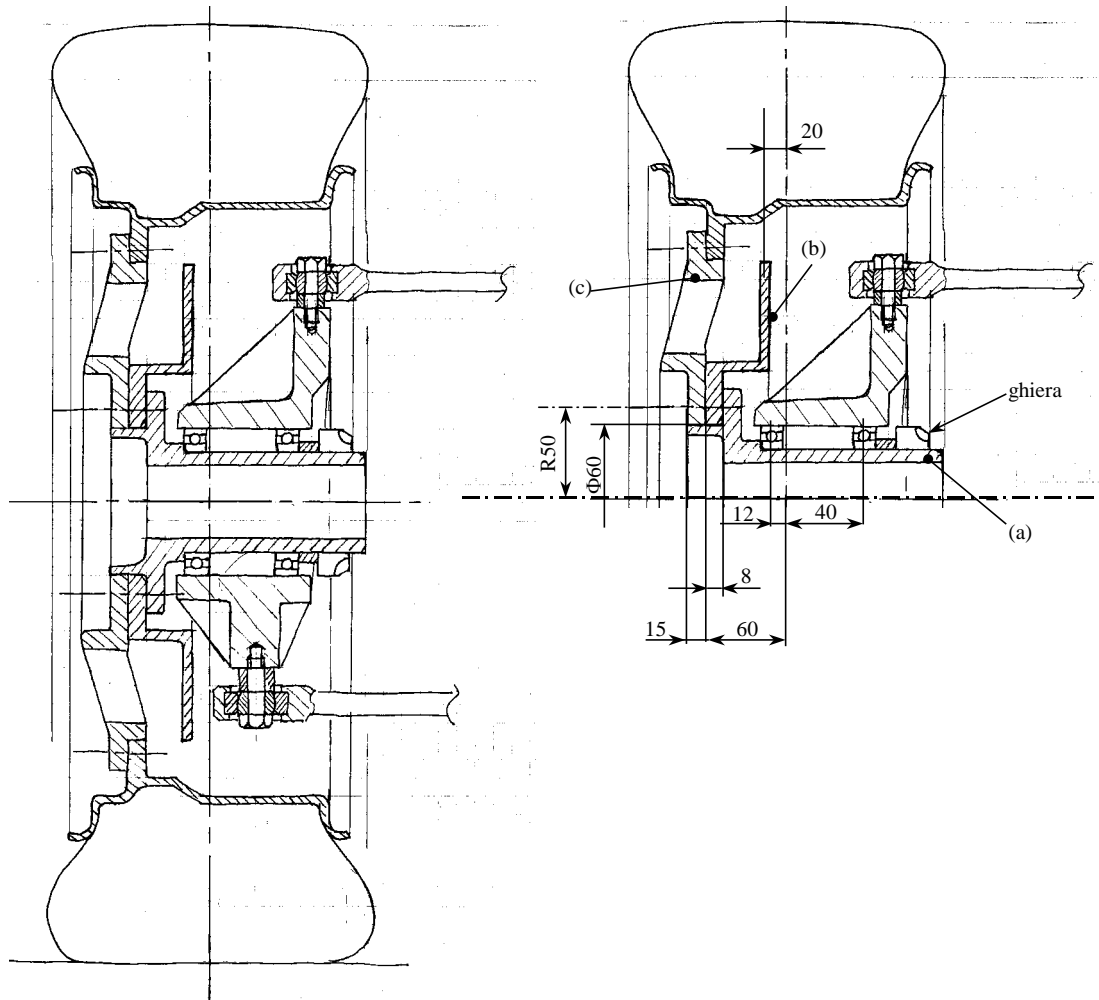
schema generale della massa non sospesa anteriore 1); particolare con dimensioni principali 2) . Il disegno non è in scala. Il disegno non rappresenta la forma costruttiva per quanto riguarda il montaggio dei cuscinetti (dimensioni in mm)
